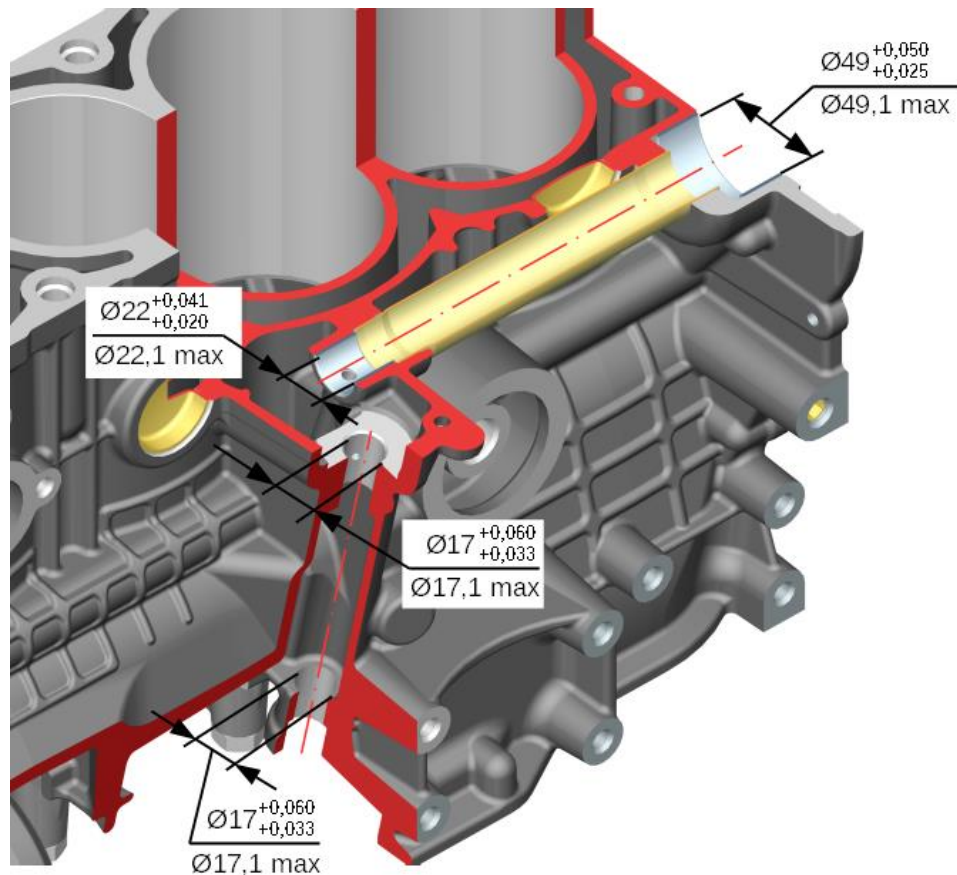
Номинальные и предельные размеры опор промежуточного вала и опор привода масляного насоса
